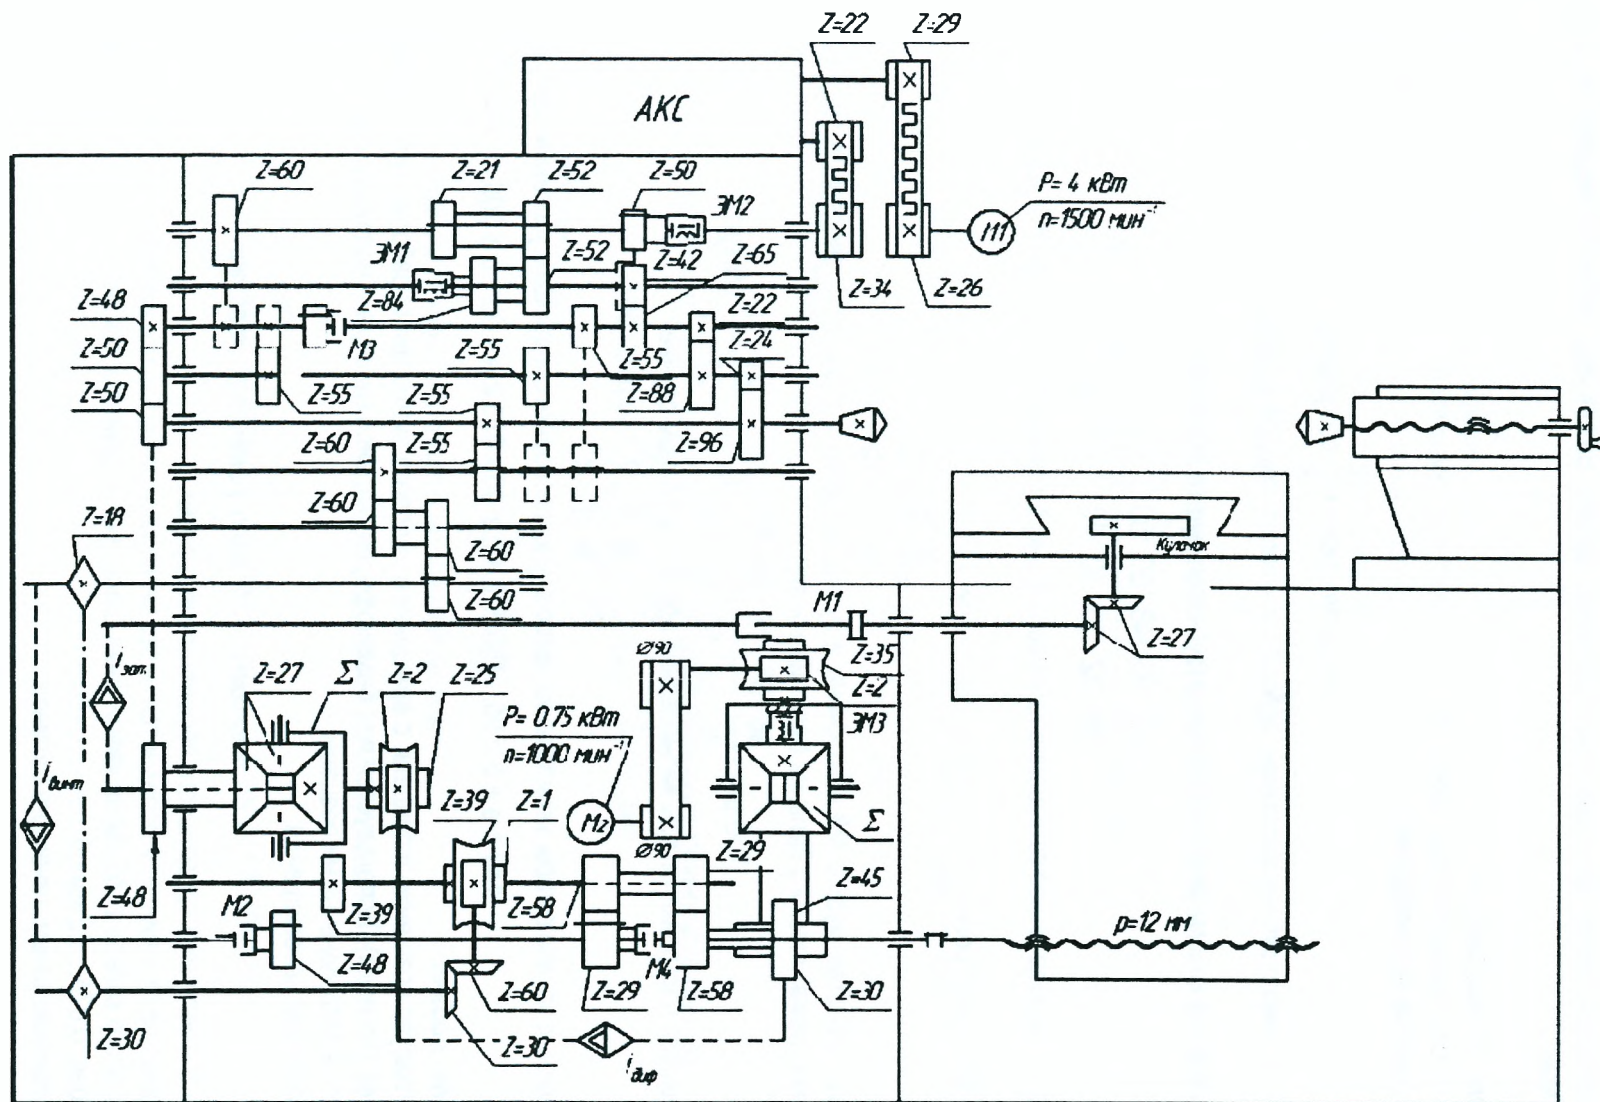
Кинематическая схема токарно-затывочного станка мод.1E811
